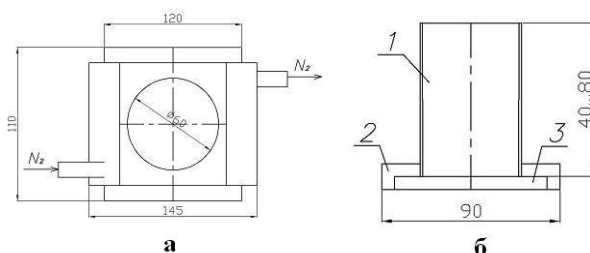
Схема реактора с размерами (в мм): а) корпус реактора; б) активные элементы реактора, 1 — кварцевый цилиндр, 2 — тефлоновое кольцо, 3 — тонкая кварцевая пластинка, 4 — кварцевый цилиндр.
